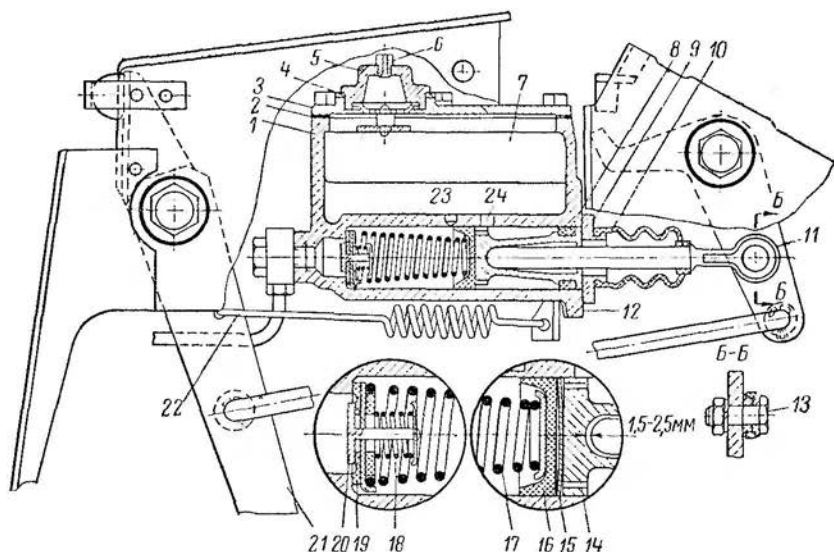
Главный цилиндр тормозов автомобиля ГАЗ-66 и его привод:
